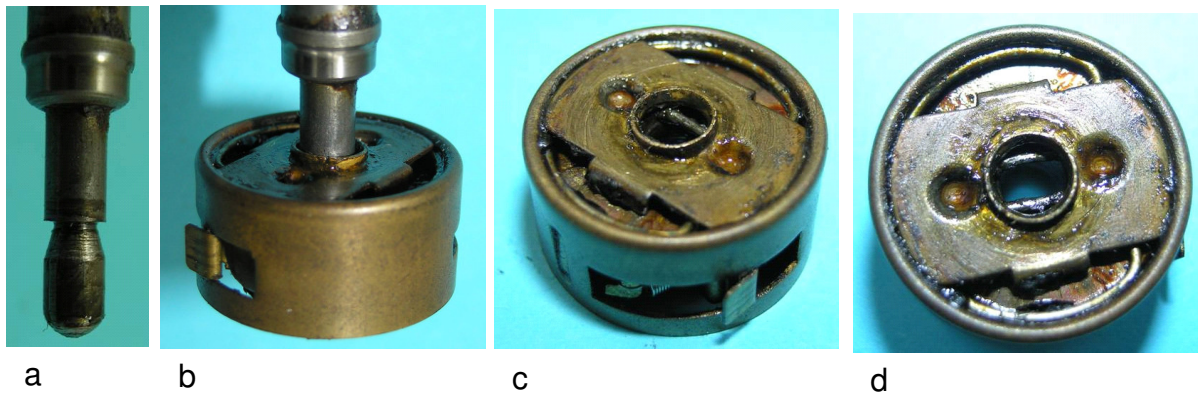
Schalterbefestigung: a) Ringnut am Wellenende mit einseitiger Schräge, b) Welle mit Schalter, c) und d) Drahtklammer
